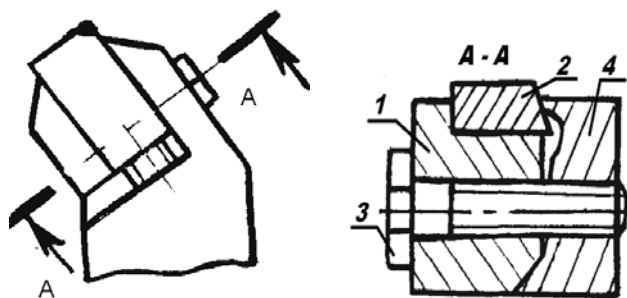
Эскиз рабочей части сборного инструмента:
